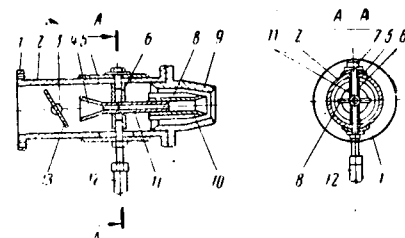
Схема горелки к устройству для разогрева вязких: 1 — фланец; 2 — корпус; 3 — ось заслонки; 4 — диффузор; 5 — крышка; 6 — направляющая втулки; 7 — винт; 8 — направляющие потока воздуха; 9 — головка; 10 — распылитель; 11 — труба; 12 — топливопровод; 13 — дисковая заслонка
